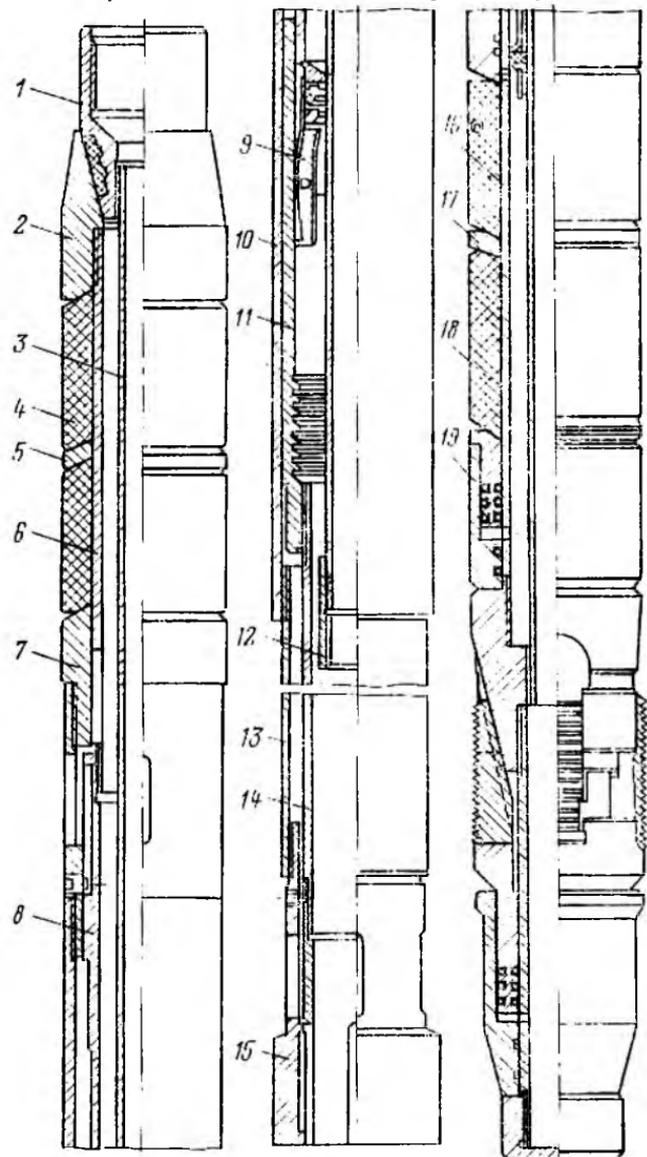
Пакер клапанный интервальный КПИ-500
